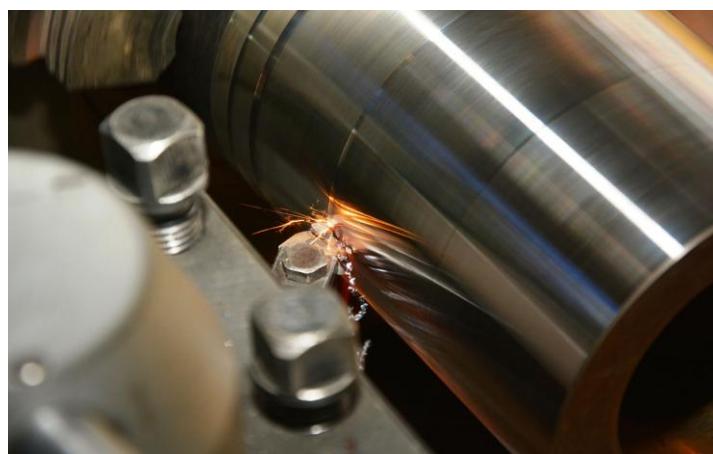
Обработка заготовки из стали 35 ХГСА металлообрабатывающим инструментом с пластинами из сверхтвердого наноструктурного КМ, закрепленными к державке методом вакуумной пайки
